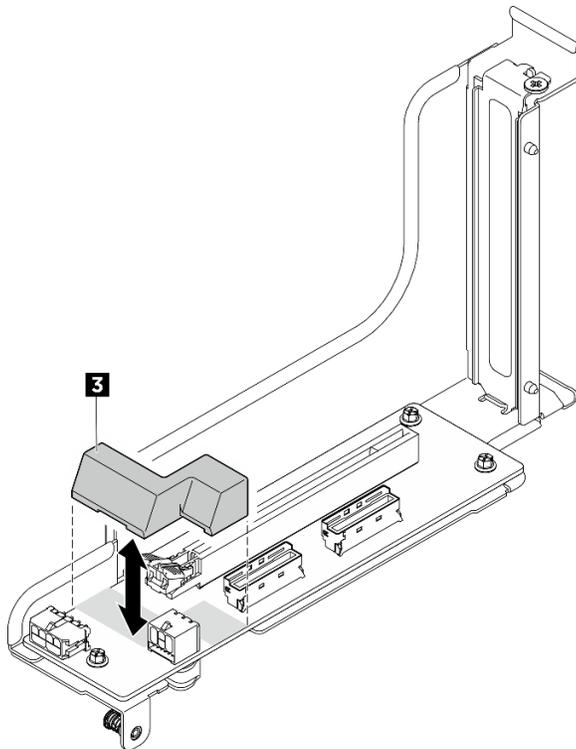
Removendo o defletor de ar da DPU da placa riser PCIe
